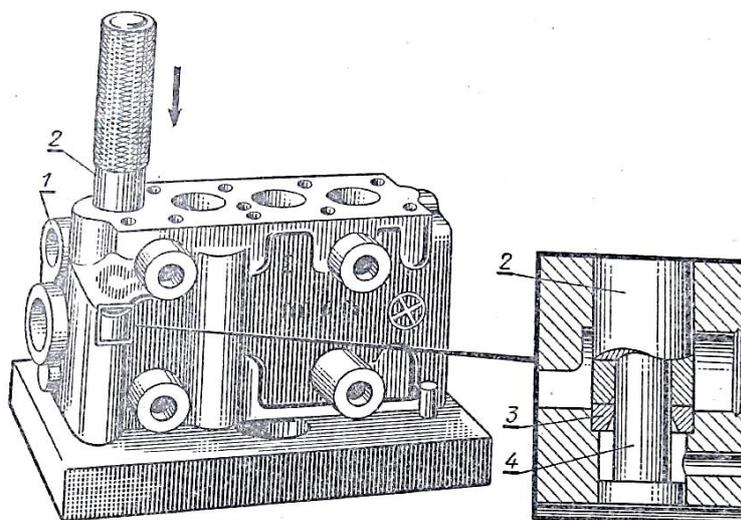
Запрессовка седла перепускного клапана: 1 – корпус распределителя; 2- оправка; 3 - седло перепускного клапана; 4 -направляющий стержень
